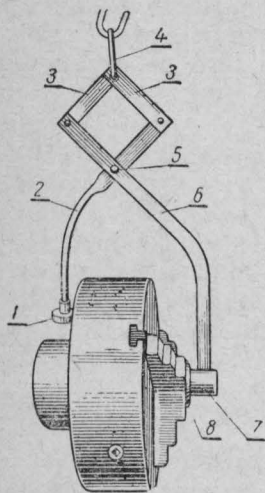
Захватное приспособление для установки и снятия кулачковых патронов:
